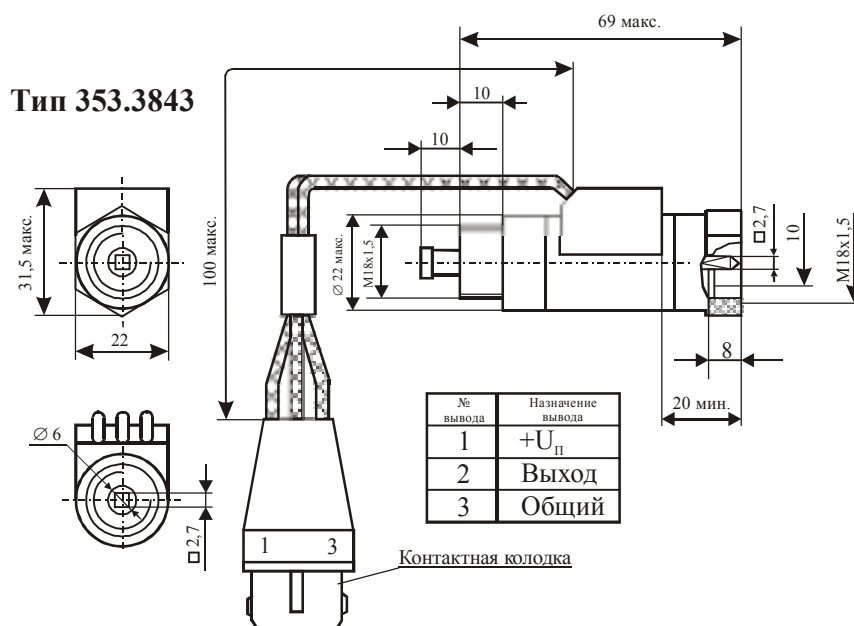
Внешний вид и габаритные размеры датчиков типа 353.3843
